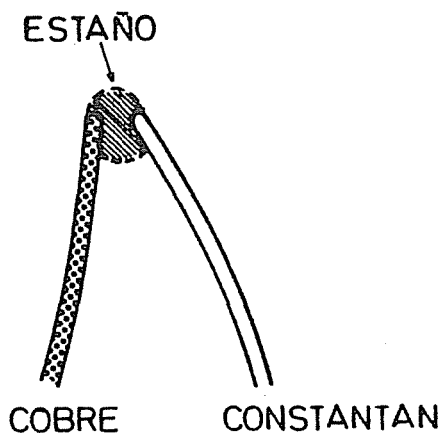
Soldadura cobre-constantán con aporte de estaño.
